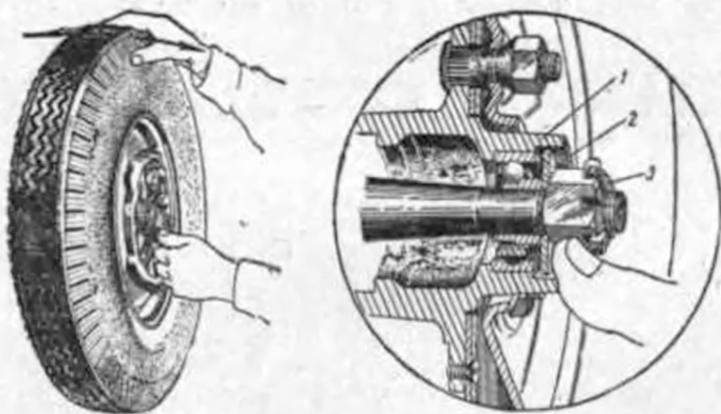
Проверка подтяжки подшипников ступицы переднего колеса
